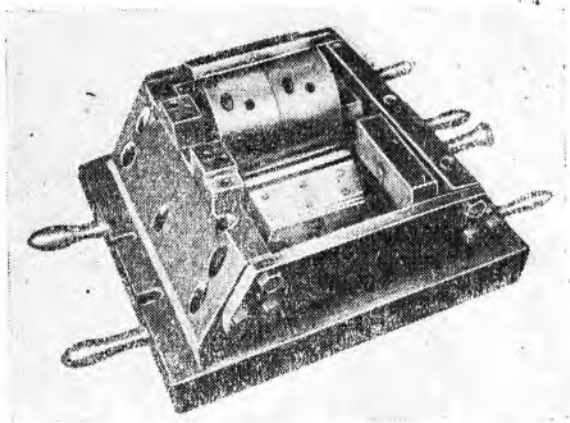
Схема фрезерования корпуса кулачкового патрона по новому технологическому процессу
